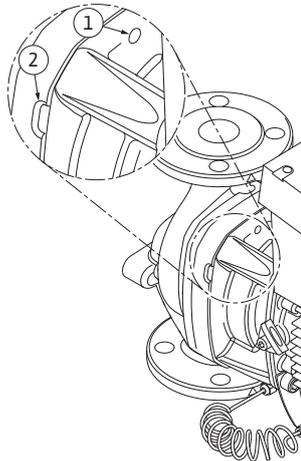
Gewindebohrungen und Schlitze zum Abdrücken des Einstecksatzes vom Pumpengehäuse
